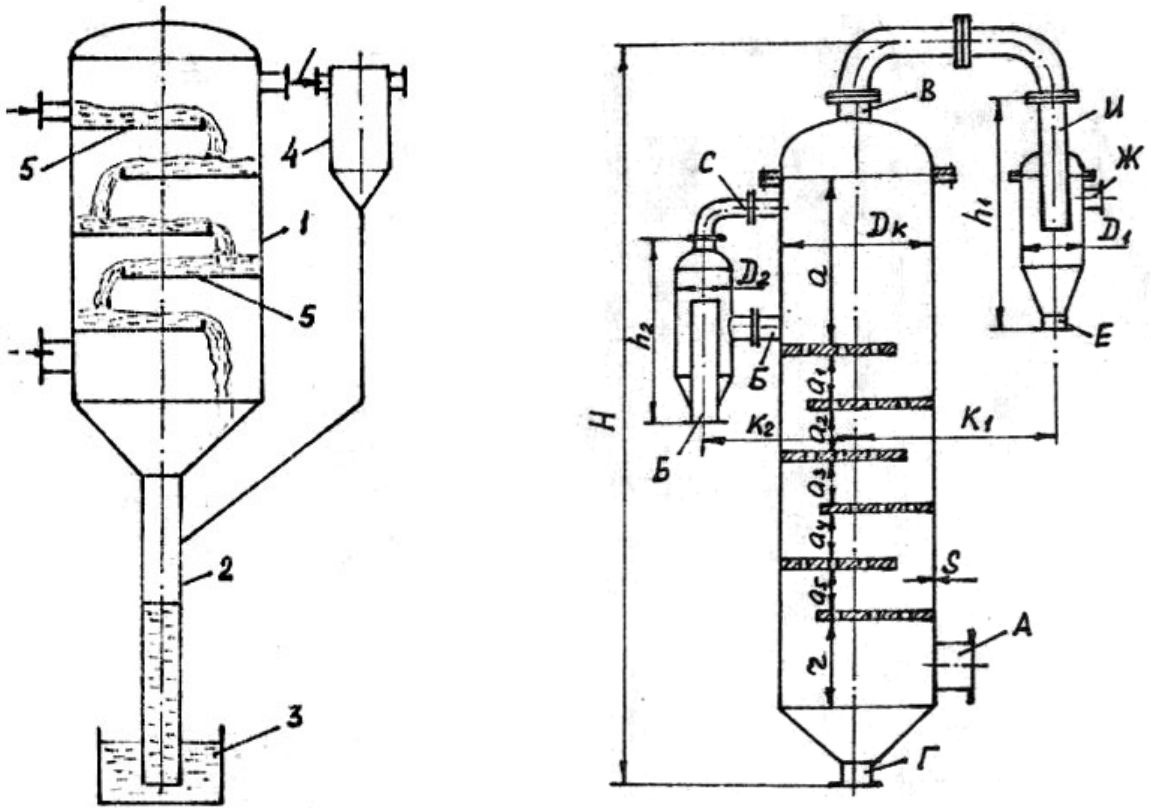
Барометрический сухой конденсатор смешения: 1-корпус; 2-барометрическая труба; 3- приемок; 4- ловушка для капель; 5- полки
